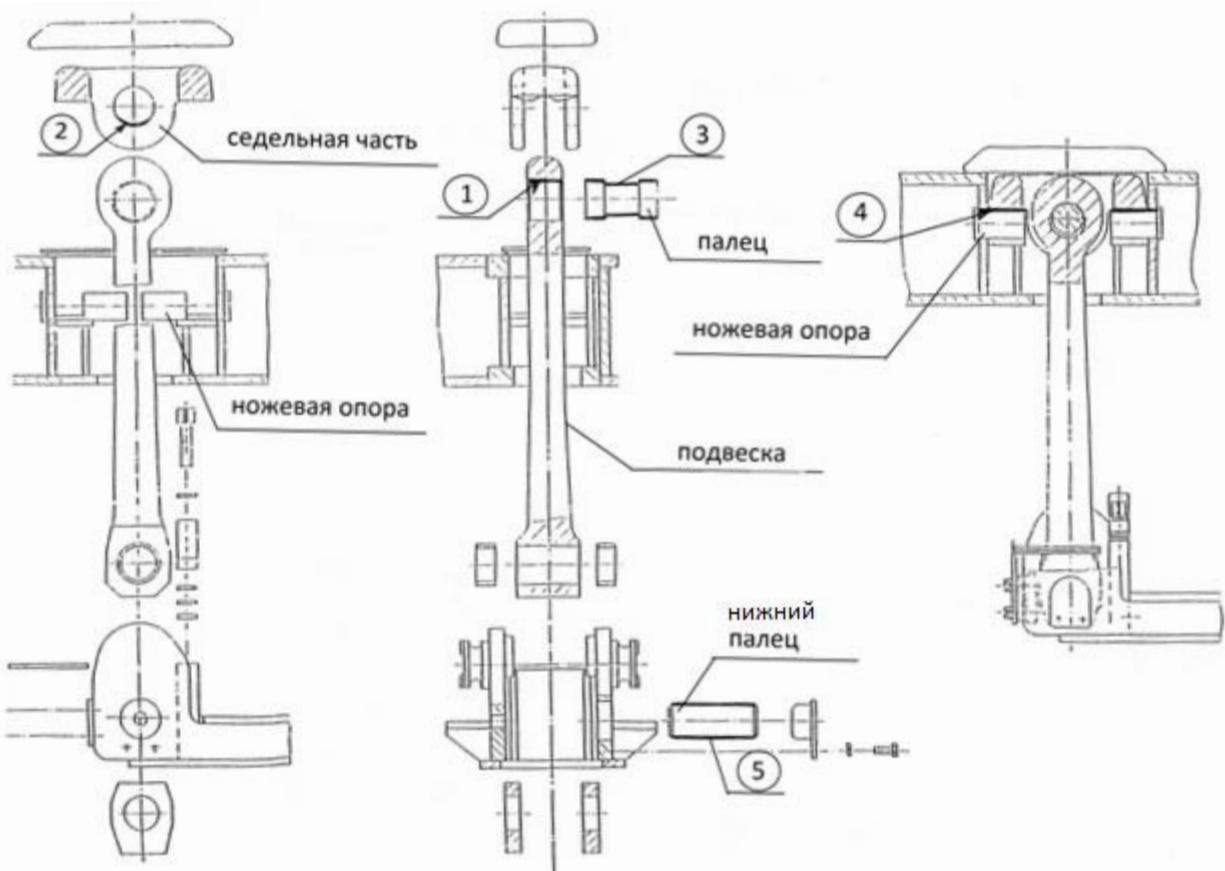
Дефекты деталей тележки GP-200, ремонтируемые сваркой или наплавкой
